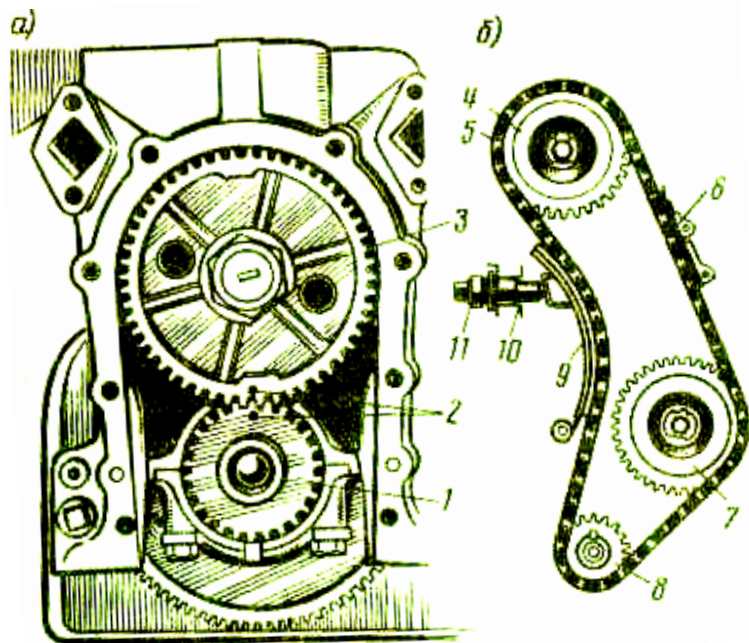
Типы привода распределительного вала: а — зубчатый; б — цепной
